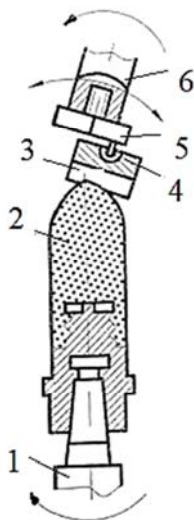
Схема полирования вогнутой поверхности заготовки линзы:
